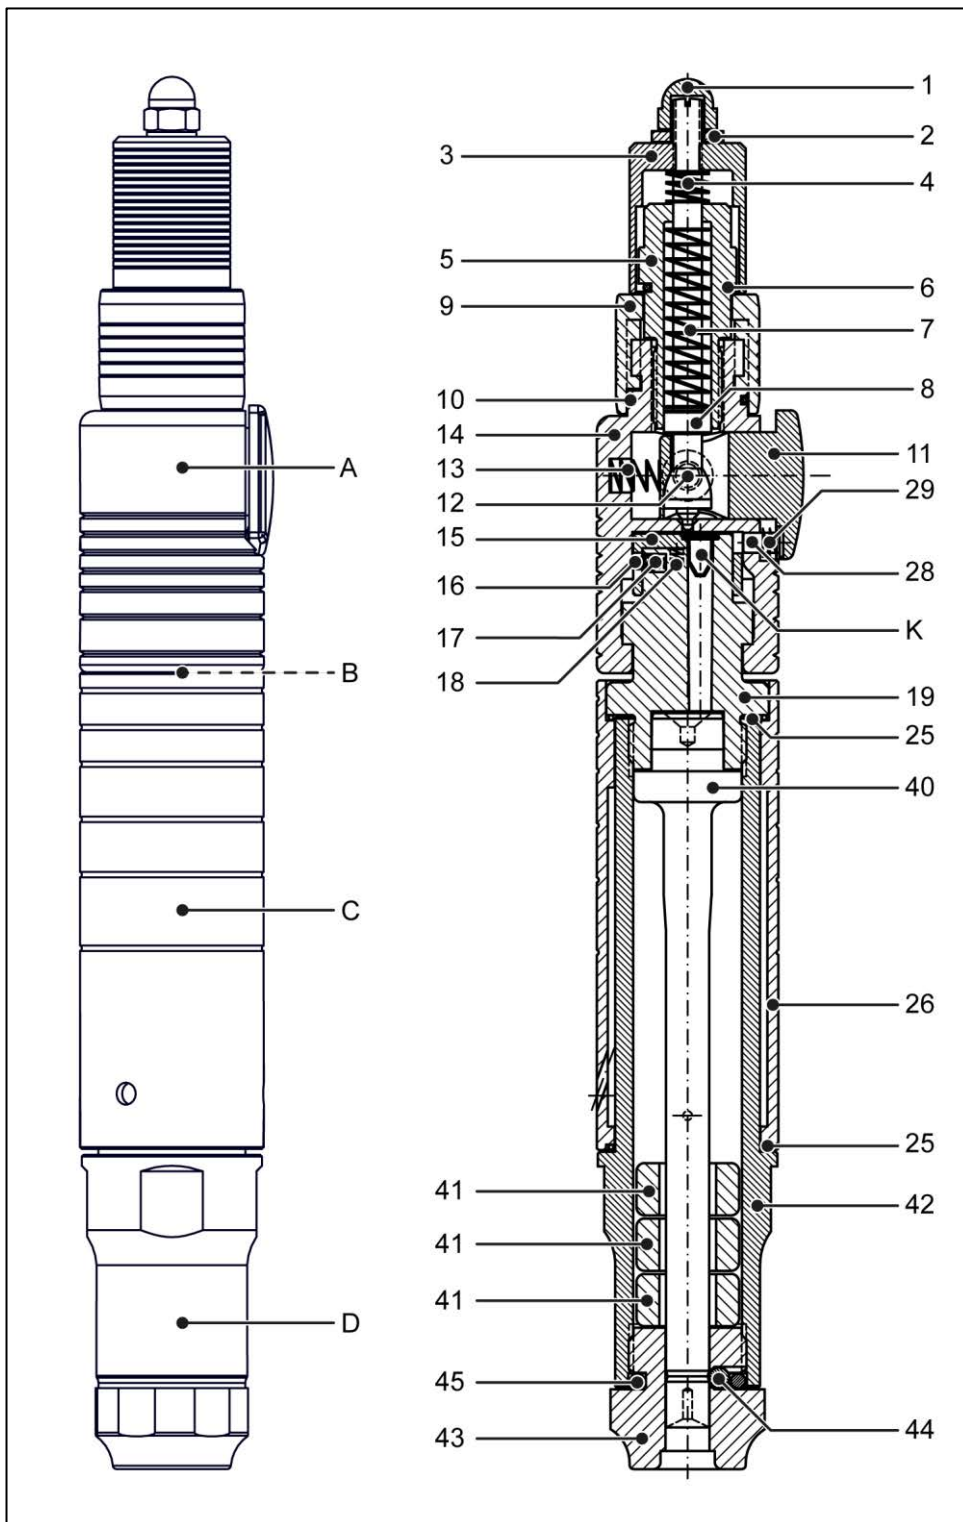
Baugruppen/Bauelemente Typ KR
